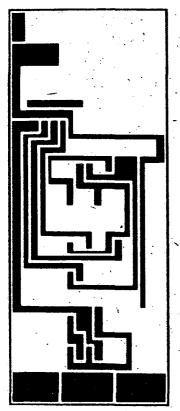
Obrazec plošných spojů desky T120 pro týdenní program (strana součástek)
